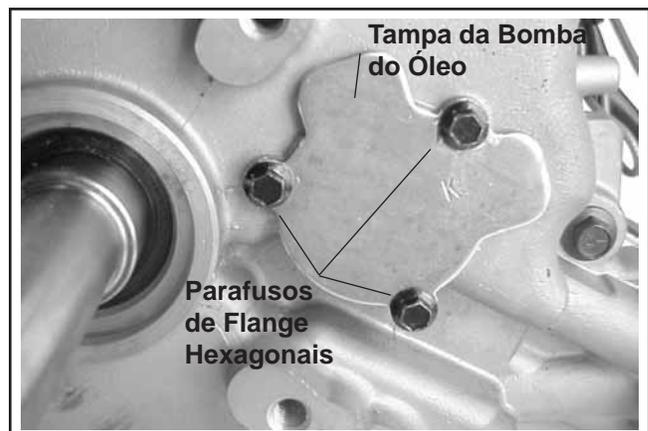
Instalar a Tampa da Bomba do Óleo.
